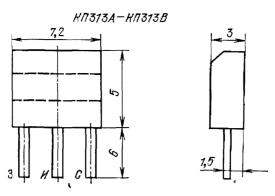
Габаритный чертеж для траизисторов КПЗ13
